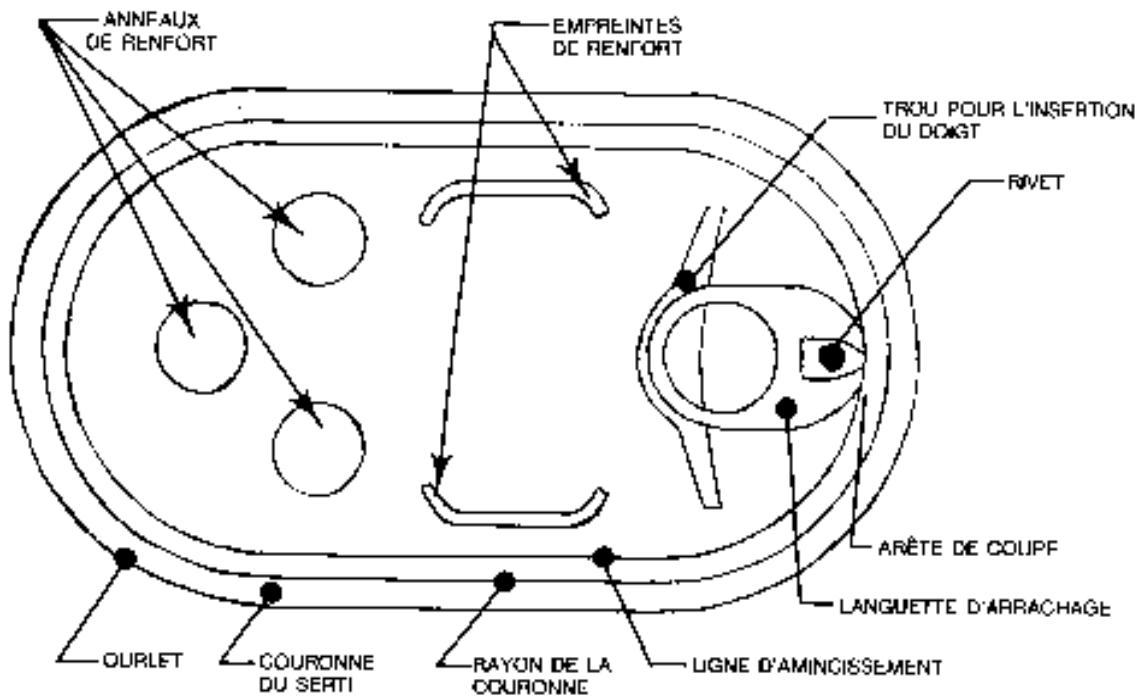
b - Fermeture de boîte à ouverture facile - Type Hansa
